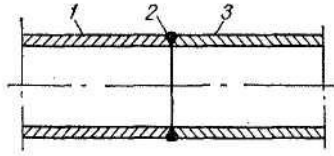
Соединение труб сваркой встык: 1, 3 – трубы; 2 – сварка
